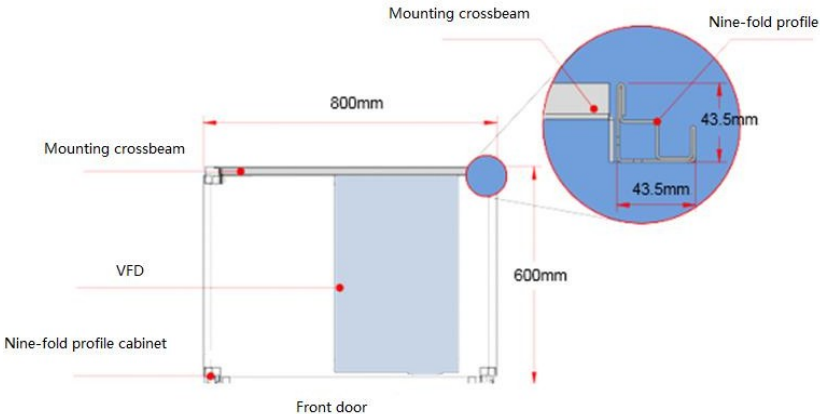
Vista superior da montagem de um VFD GD270 280-500kW em um gabinete
